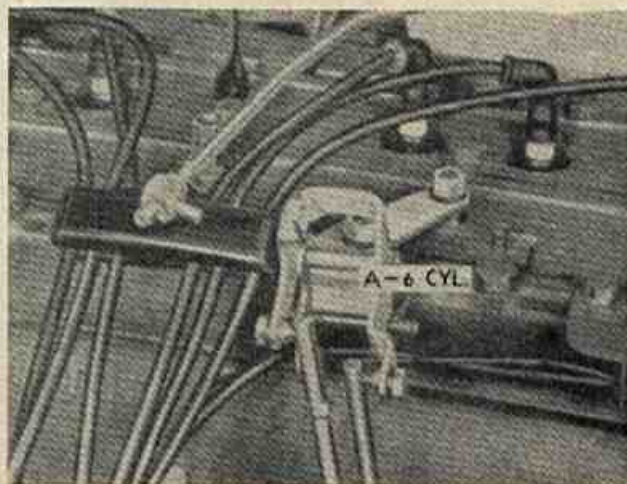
O pino ajustador J-2544 instalado em A, no motor de 6 cilindros
